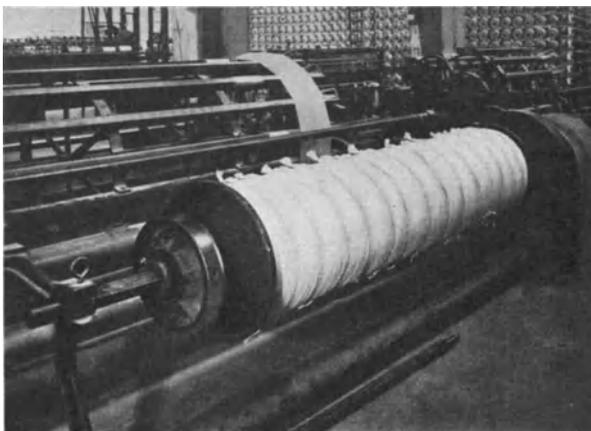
Bäummaschine mit vollem Kettenbaum.
